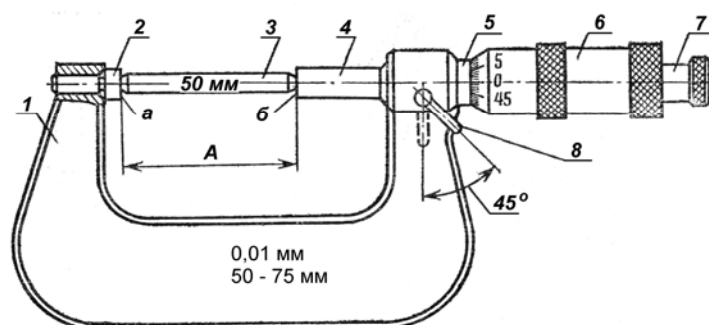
Мікрометр для зовнішніх вимірювань: 1 – скоба; 2 – жорстка п'ята; 3 – міра для установки мікрометра на нуль; 4 – рухома п'ята (мікрогвинт); 5 – стебло; 6 – мікрометрична головка; 7 – тріскотний пристрій; 8 – стопор.
